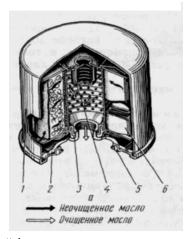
Полнопоточный фильтр для очистки масла двигателя автомобиля ВАЗ: I — корпус; 2 — дно корпуса; 3 — противодренажный клапан; 4 — перепускной клапан; 5 — уплотнительная прокладка; 6 — фильтрующий элемент
